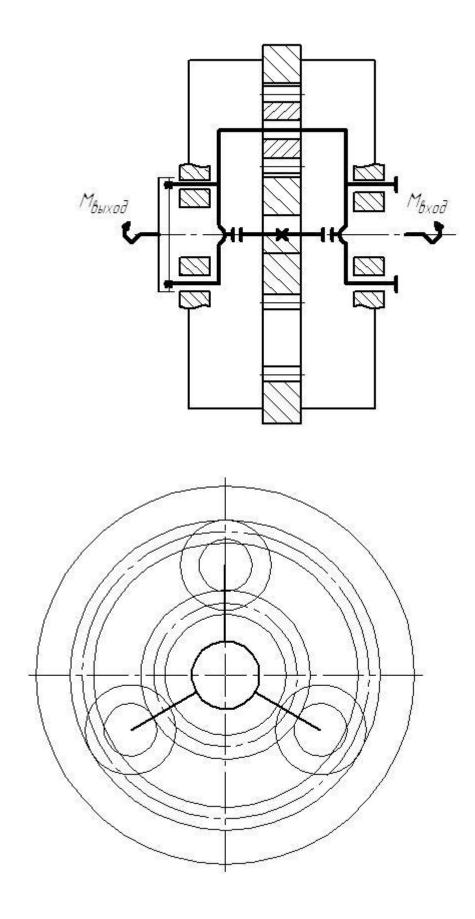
Кинематическая схема узла планетарного редуктора
